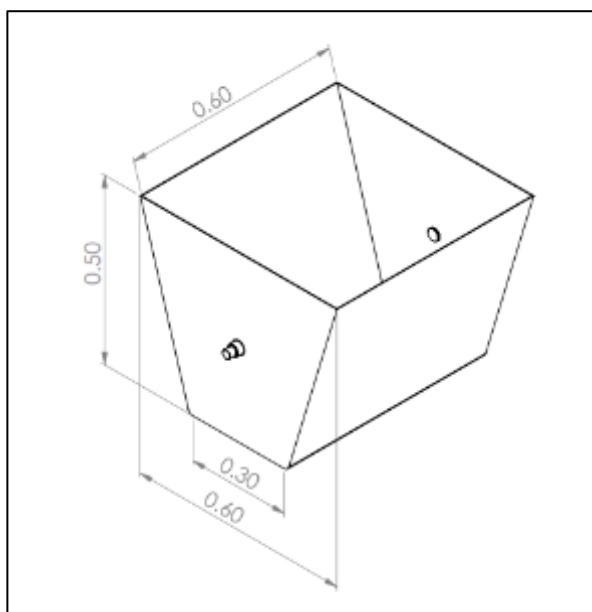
Bosquejo de la cubeta para elevar el concreto mezclado.
